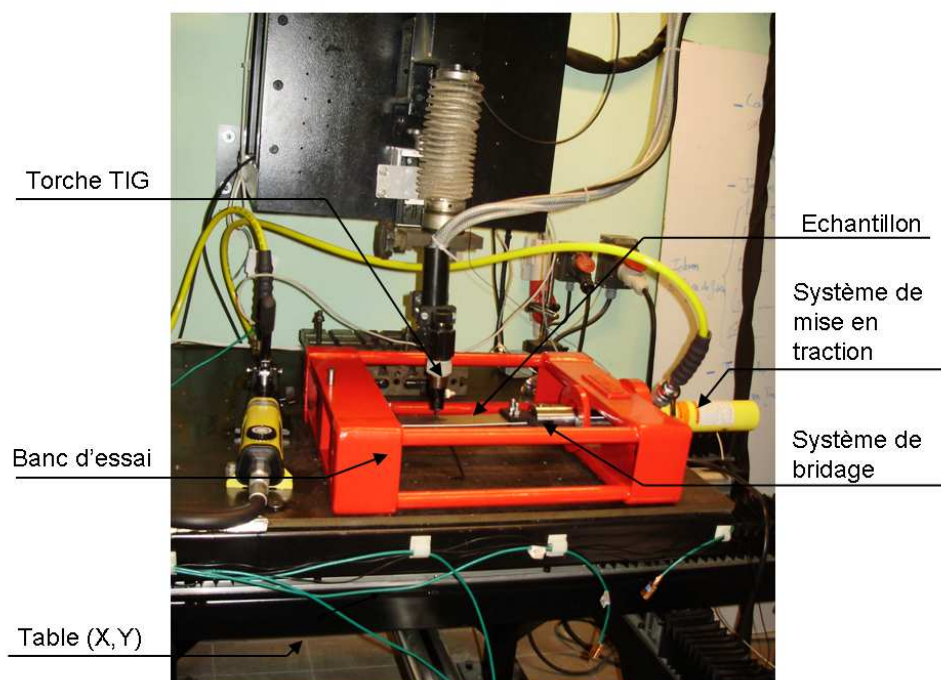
Banc d'essai de fissuration à chaud et installation de soudage
